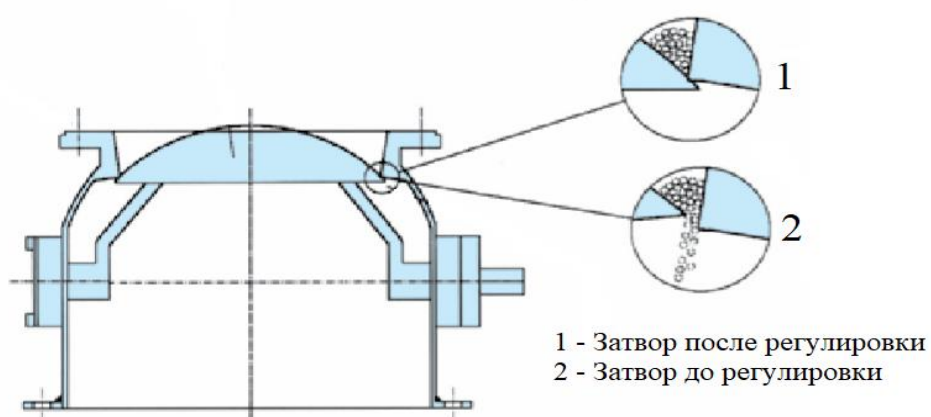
Изношенный шаровой затвор до и после регулировки запорного элемента
